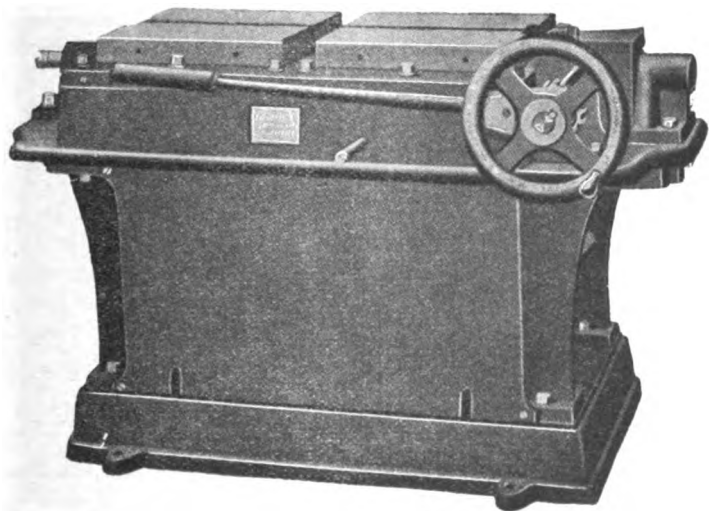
Banco di lavoro per macchine per la saldatura elettrica.
